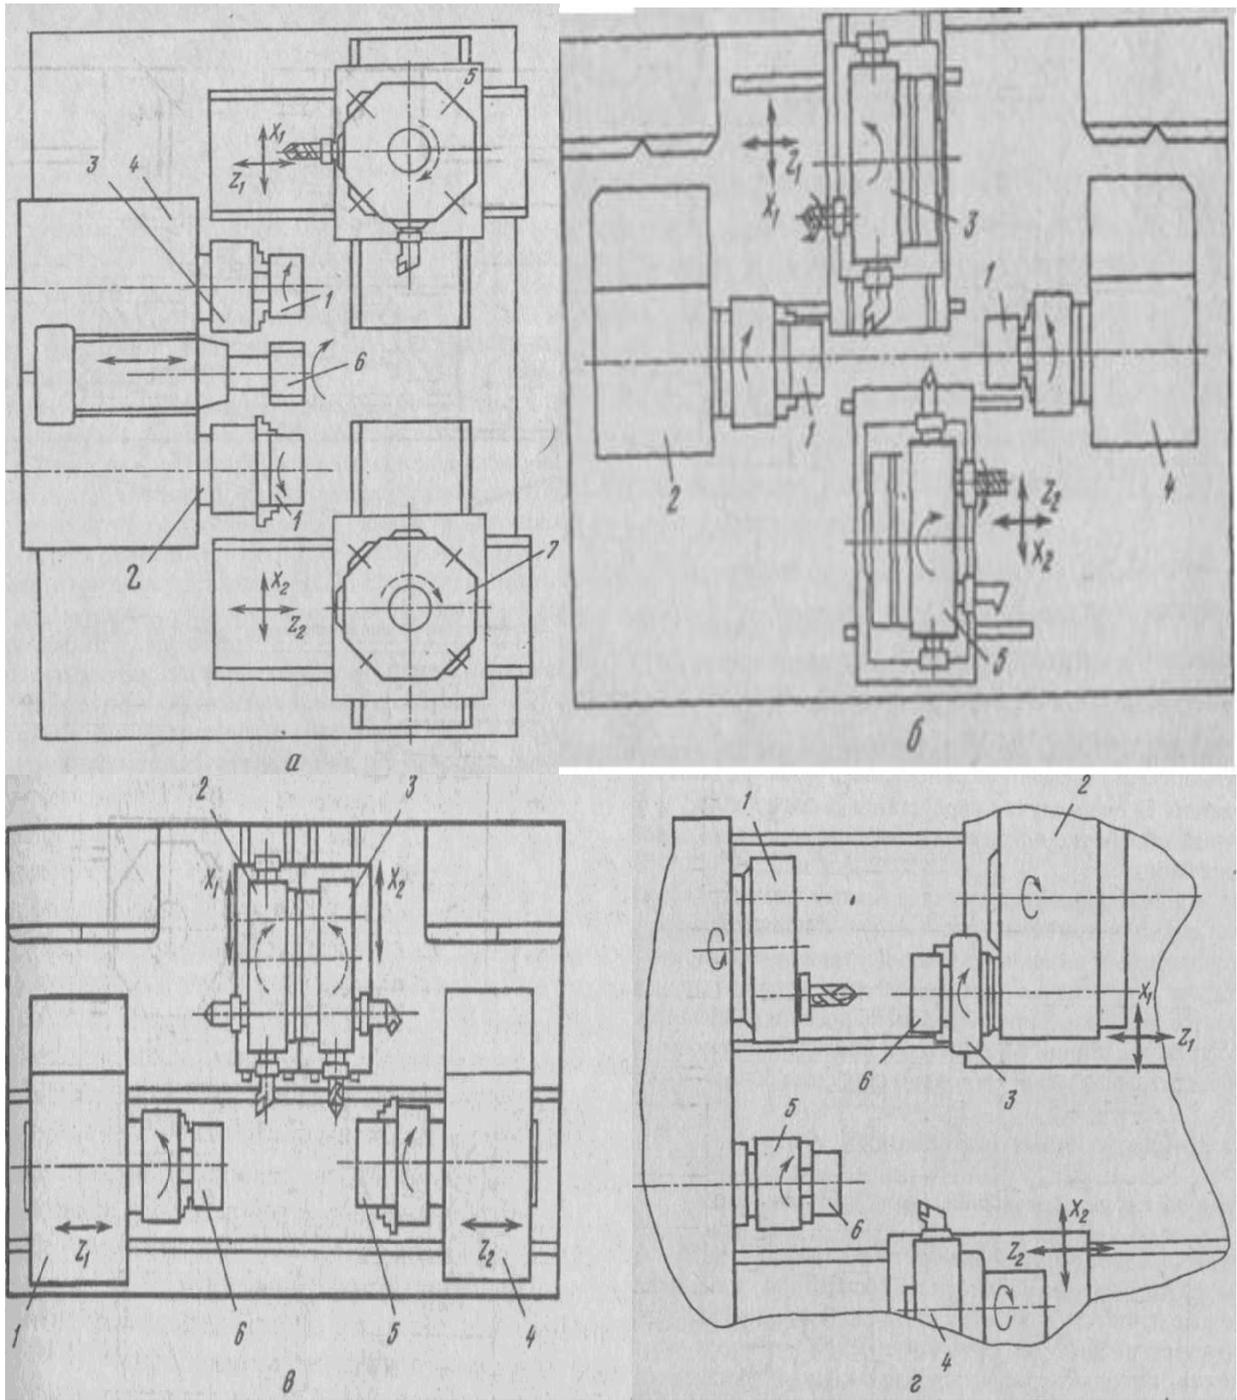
Компонентные схемы двухшпиндельных станков: а – с параллельным расположением шпинделей, б – с оппозитным расположением шпинделей, в – с перемещающимися шпиндельными бабками, г – с дополнительным шпинделем в револьверной головке.
